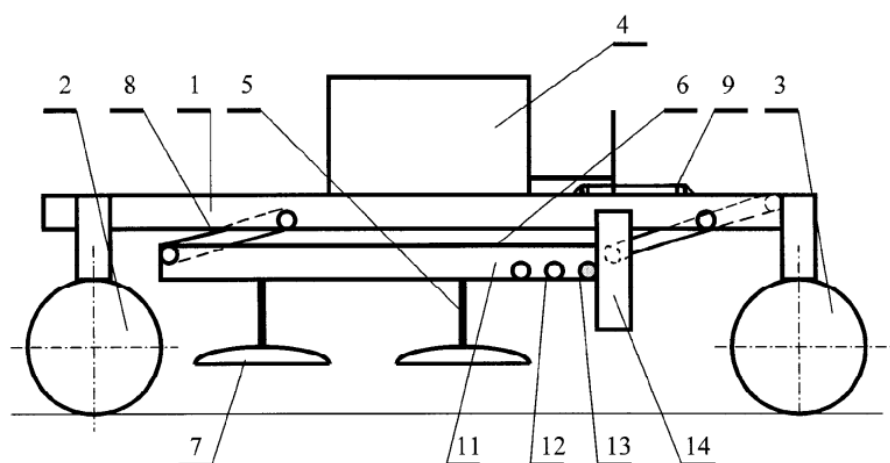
Ґрунтообробно-висіваючий агрегат: 1 – корпус-рама; 2 – передні колеса; 3 – задні колеса; 4 – бункер; 5 – трубчасті тримачі; 6 – додаткова рама; 7 – ріжучі диски; 8 – важелі; 9- гідравлічний циліндр; 10 – подовжений важіль; 11 – бокова сторона додаткової рами; 12- додаткові отвори; 13 – фіксатори; 14 – упори.
